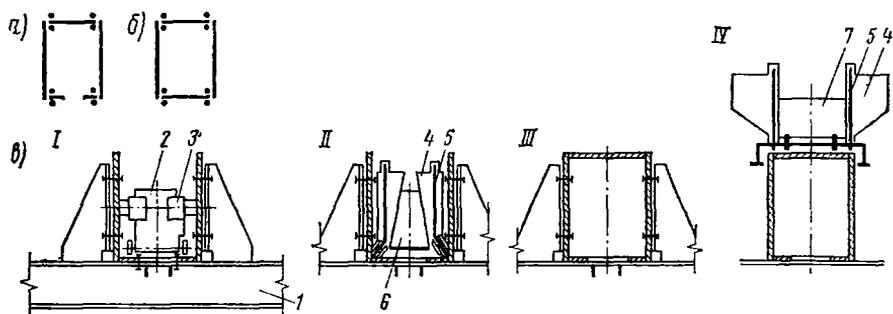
Схемы коробчатых элементов и последовательности их изготовления: I — сборка в кондукторе вертикальных и нижнего горизонтального листа; II — сварка внутренних швов; III — сборка в кондукторе верхнего горизонтального листа; IV — сварка наружных швов; 1 — кондуктор; 2 — телешка с пневмоприжимом; 3 — пневмоцилиндр; 4 — бункер с флюсом; 5 — электродная проволока; 6 — двухдуговой автомат для сварки внутренних швов; 7 — то же, наружных швов
